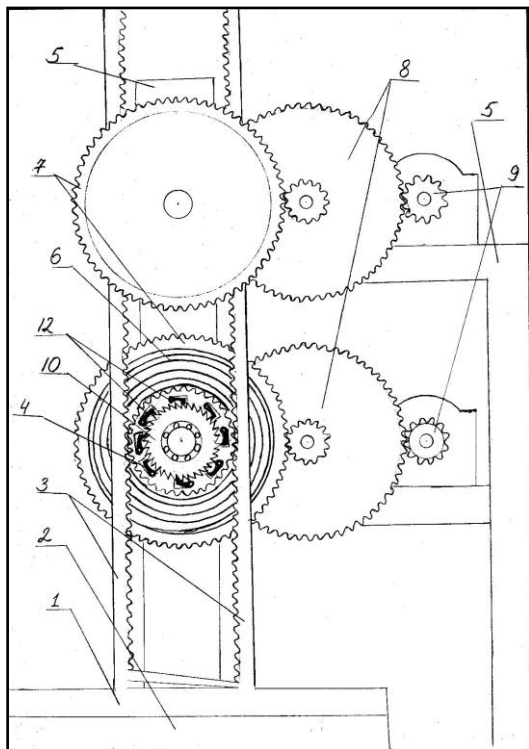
Волновой преобразователь передача с помощью зубчатой рейки, вид спереди.
